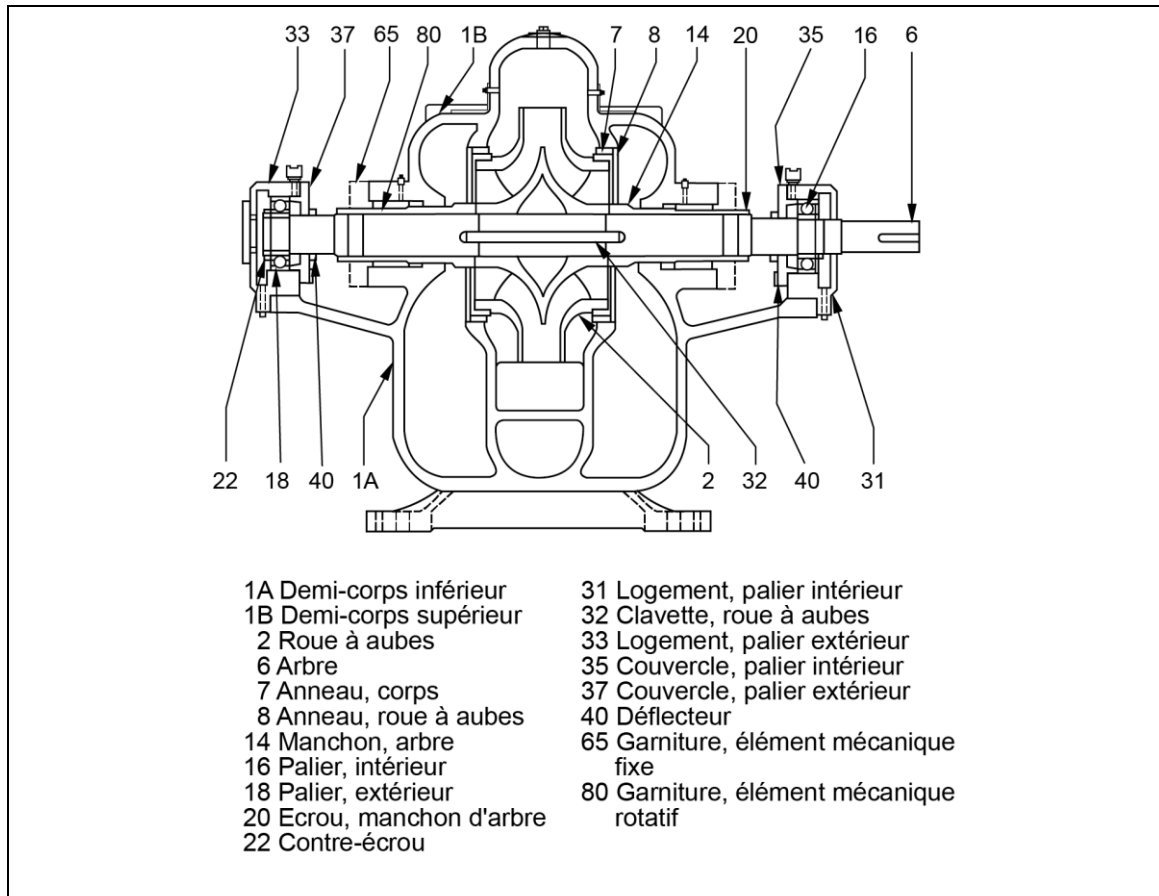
Vue en coupe d'une pompe à plan de joint horizontal type
